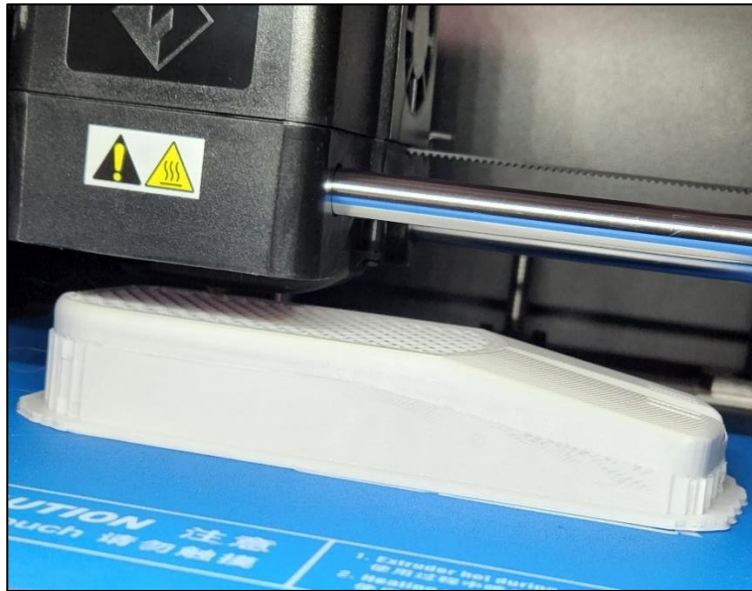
Impresión en 3D de la tapa del dispositivo
